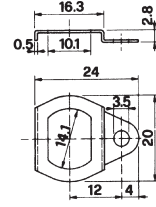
Flansch mit einseitiger Befestigung, gekröpft
